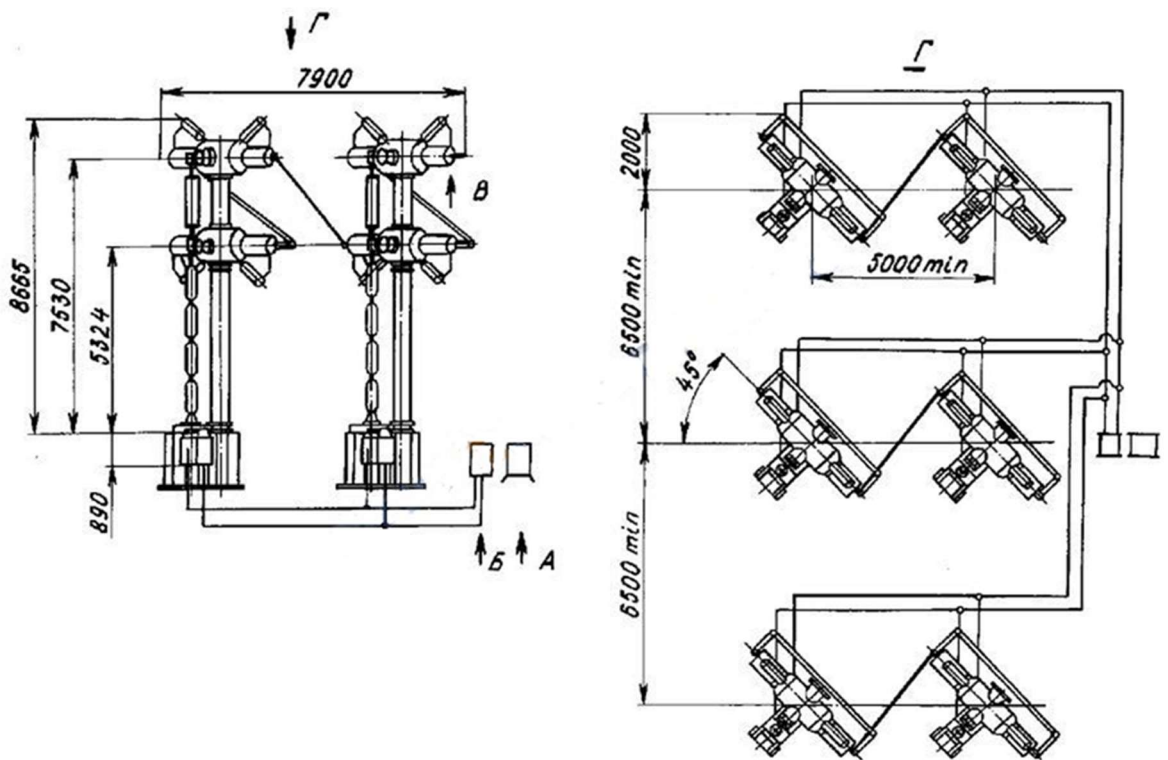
Габаритные размеры трехполюсного комплекта выключателя ВВБК-500
